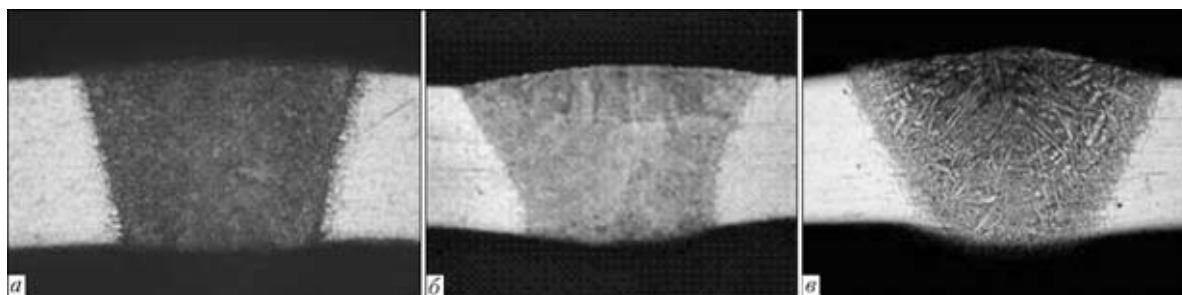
Макрошлифы (×20) сварных стыковых соединений, полученных орбитальной ЭЛС за два прохода: а — сталь 304SS; б — титановый сплав ПТ-3В; в — сплав монель
